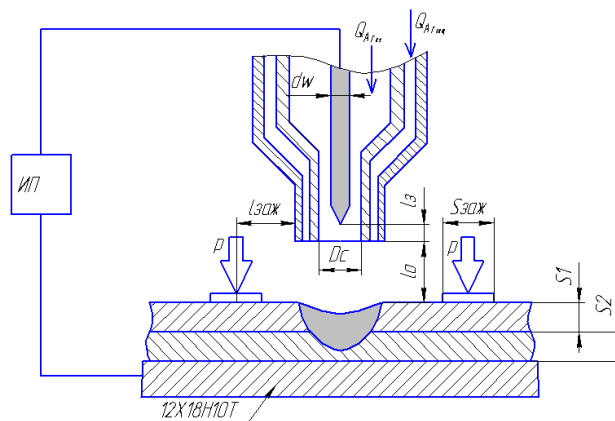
Эскиз плазмотрона для сварки сжатой дугой
